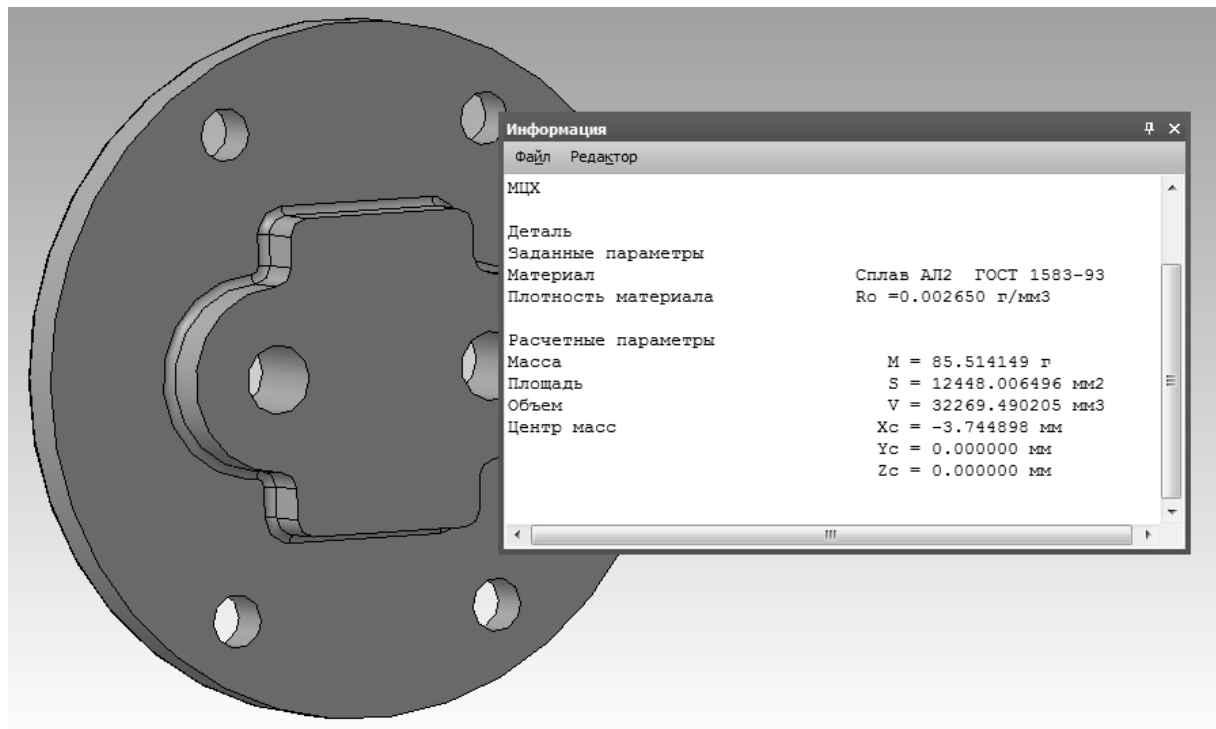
Характеристики заготовки при литті під тиском
